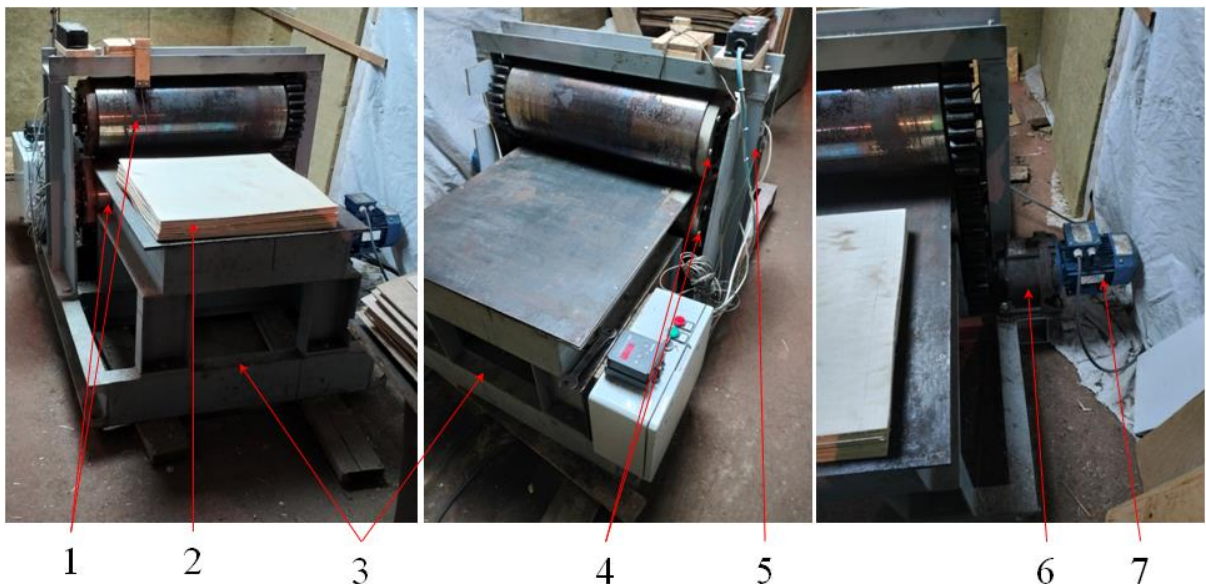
Прокатный стан: 1 – вальцы, 2 – шпон, 3 – рама, 4 – теплоэлектронагреватели (ТЭН), 5 – механизм регулировки зазора, 6 – редуктор, 7 – электродвигатель
